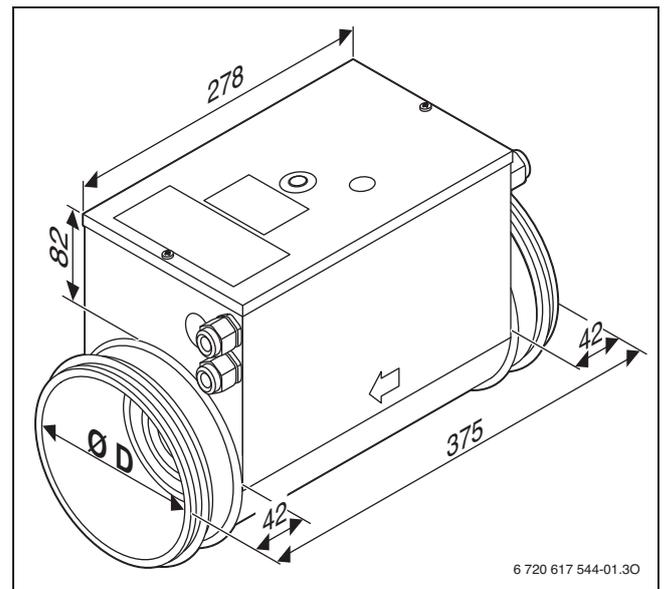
Dimensioni di montaggio della batteria di riscaldamento HRE 125/160 (in mm)
